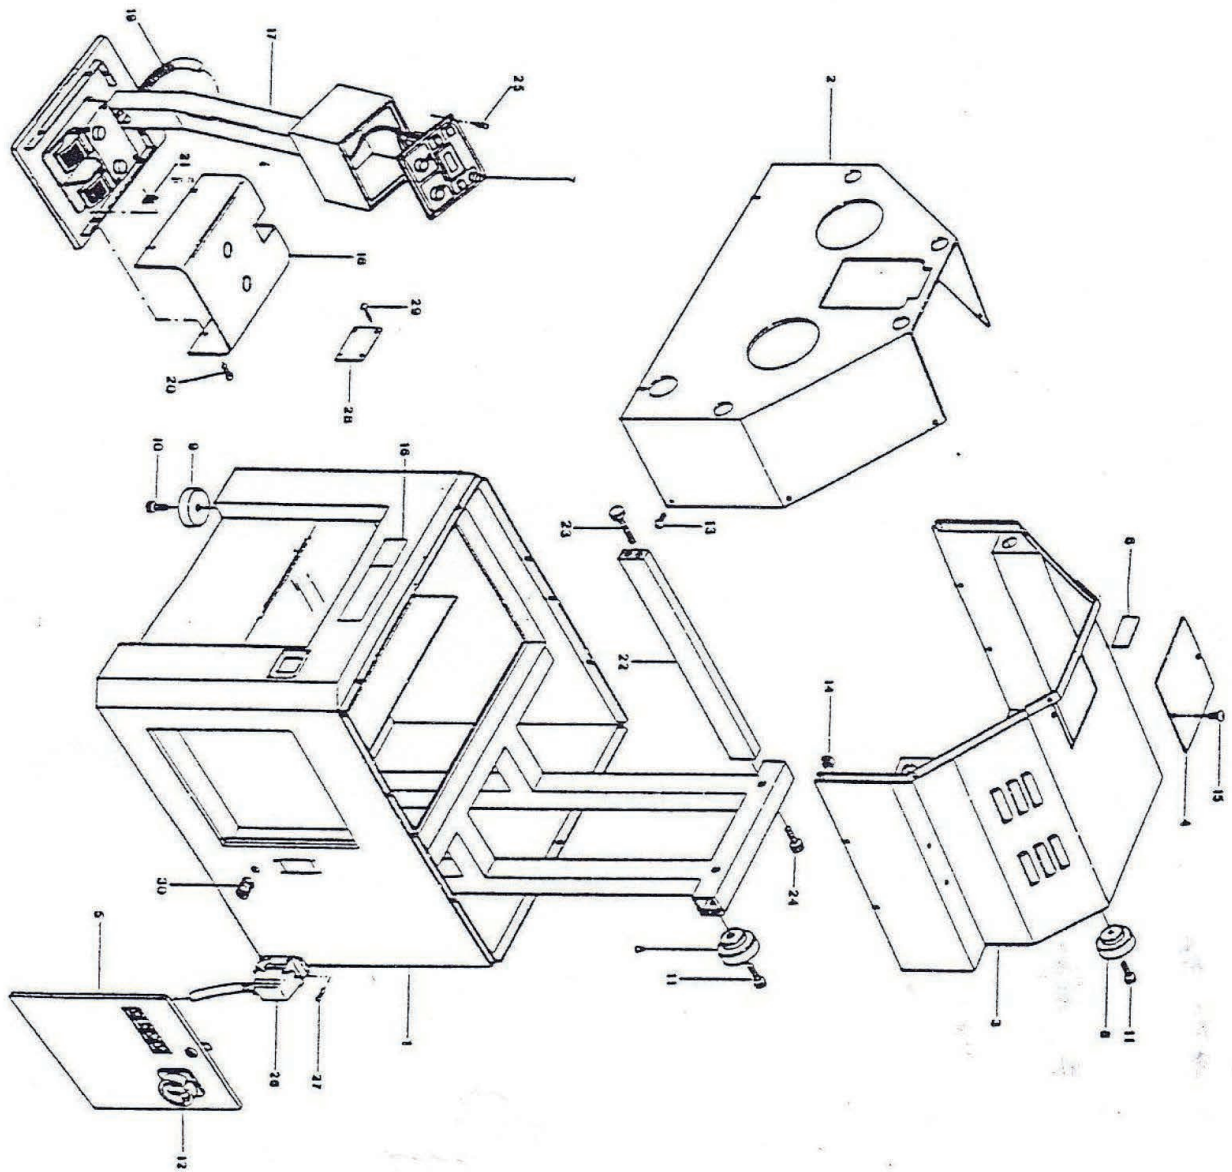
Dessin des pièces détachées PRM 60 FH
